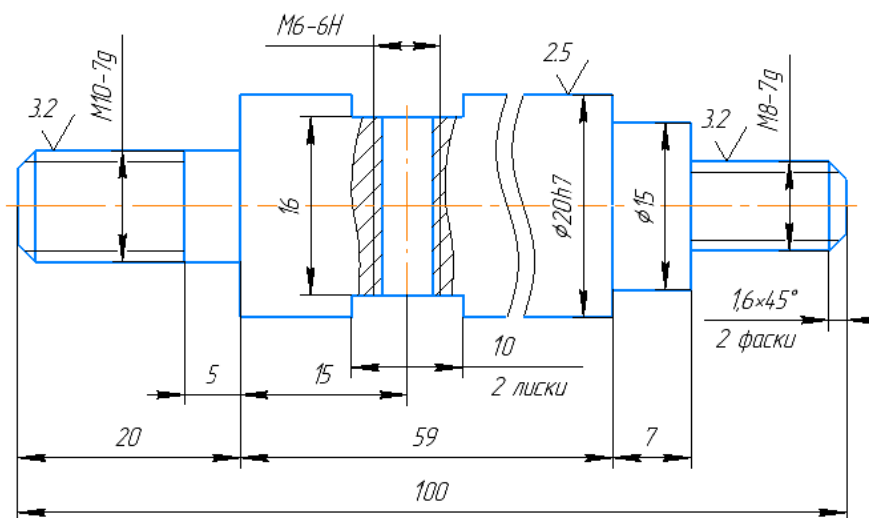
Вісь машини для виготовлення із багатошарових полімерних плівок упаковок типу дой-пак
